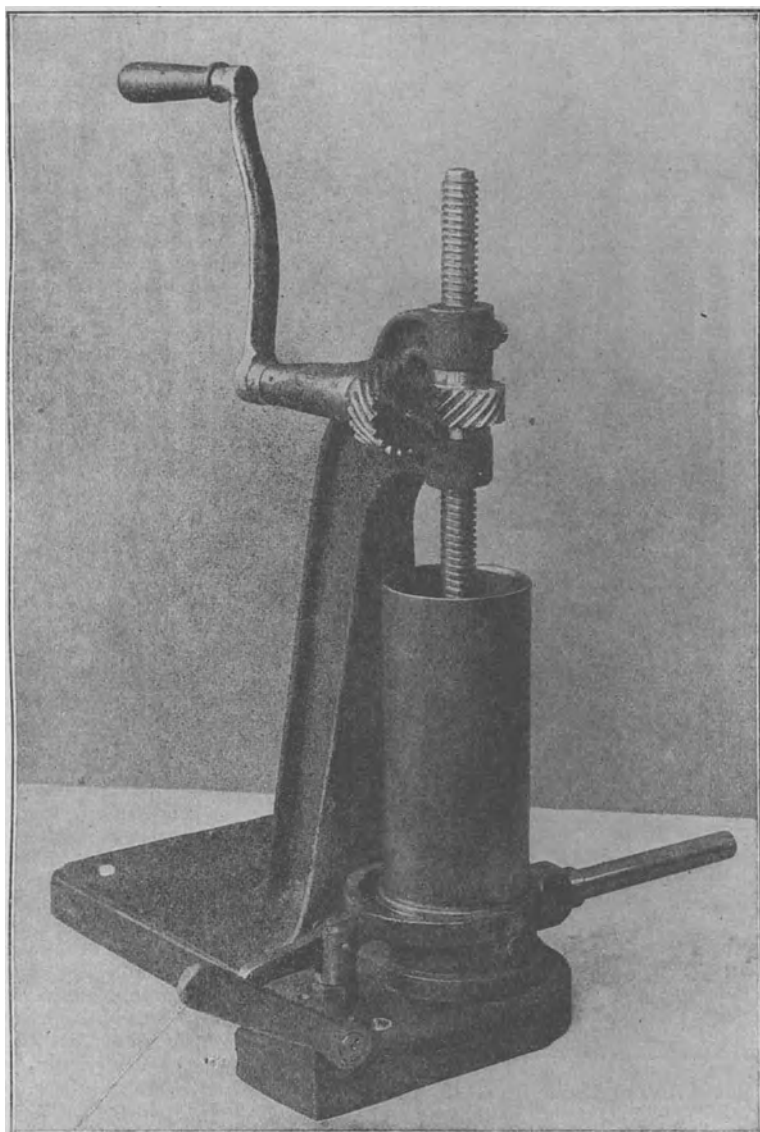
Tubenfüllmaschine für Handbetrieb.
